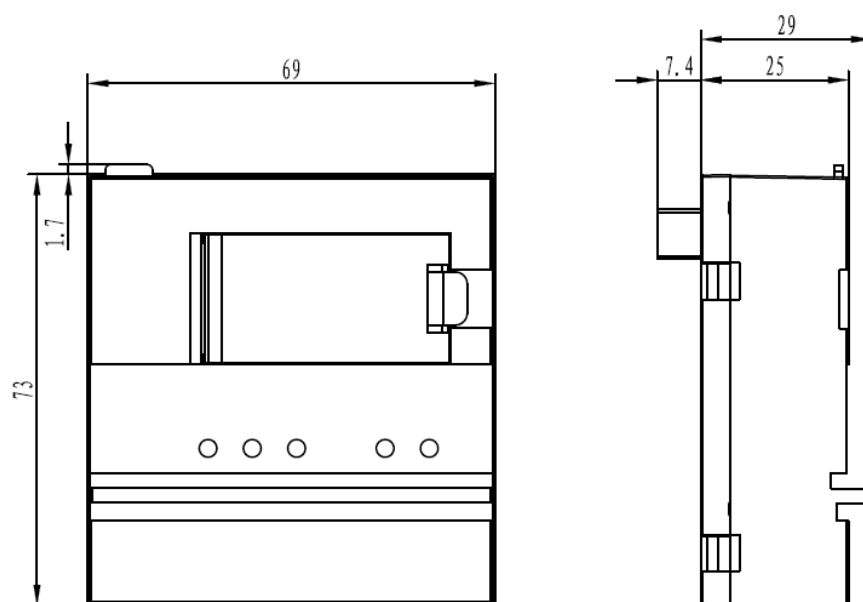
Габаритные размеры БВПД GPRS
